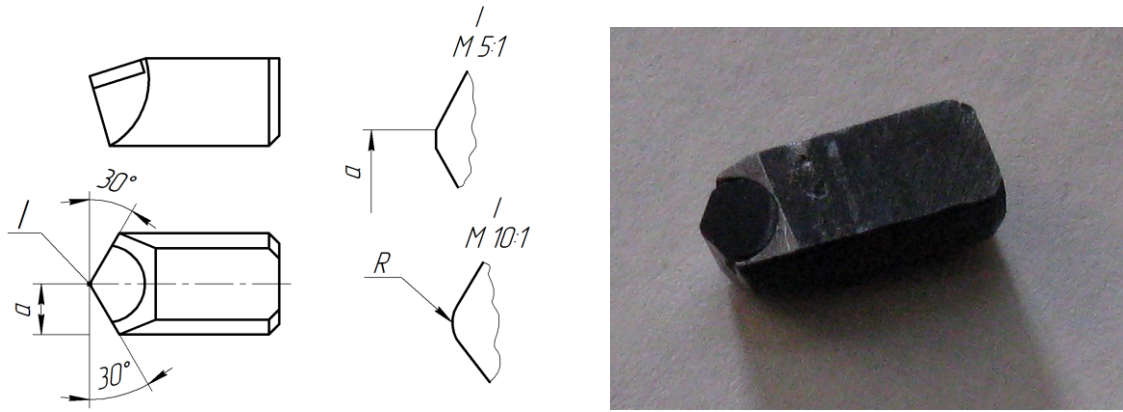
Конструкция и общий вид универсальной резцовой вставки с напаянной пластинкой СТМ «Белбор»
